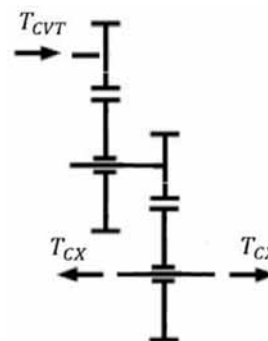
Fluxo de Potência caixa redutora de engrenagens.
